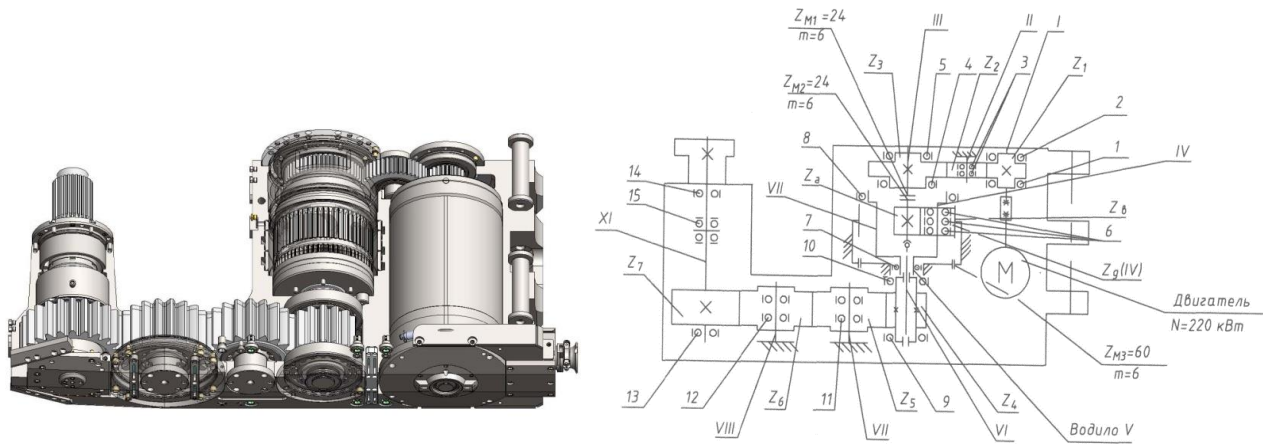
Корпус у розрізі та кінематична схема редуктора різання очисного комбайна УКД200-500.
